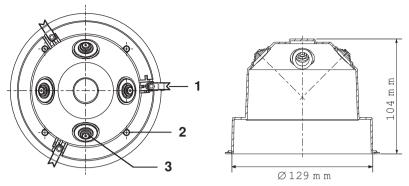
Vista en planta y vista lateral de la caja posterior para montaje en el techo FAA-500-BB
